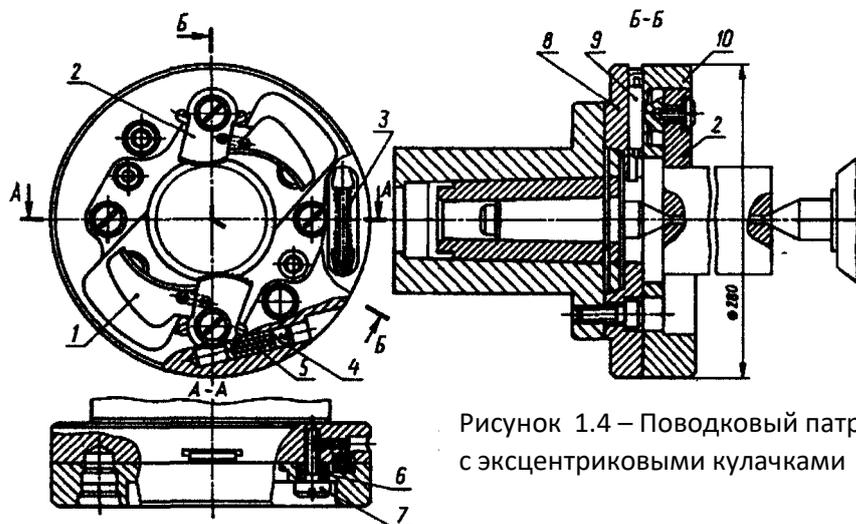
Поводковый патрон с эксцентриковыми кулачками
